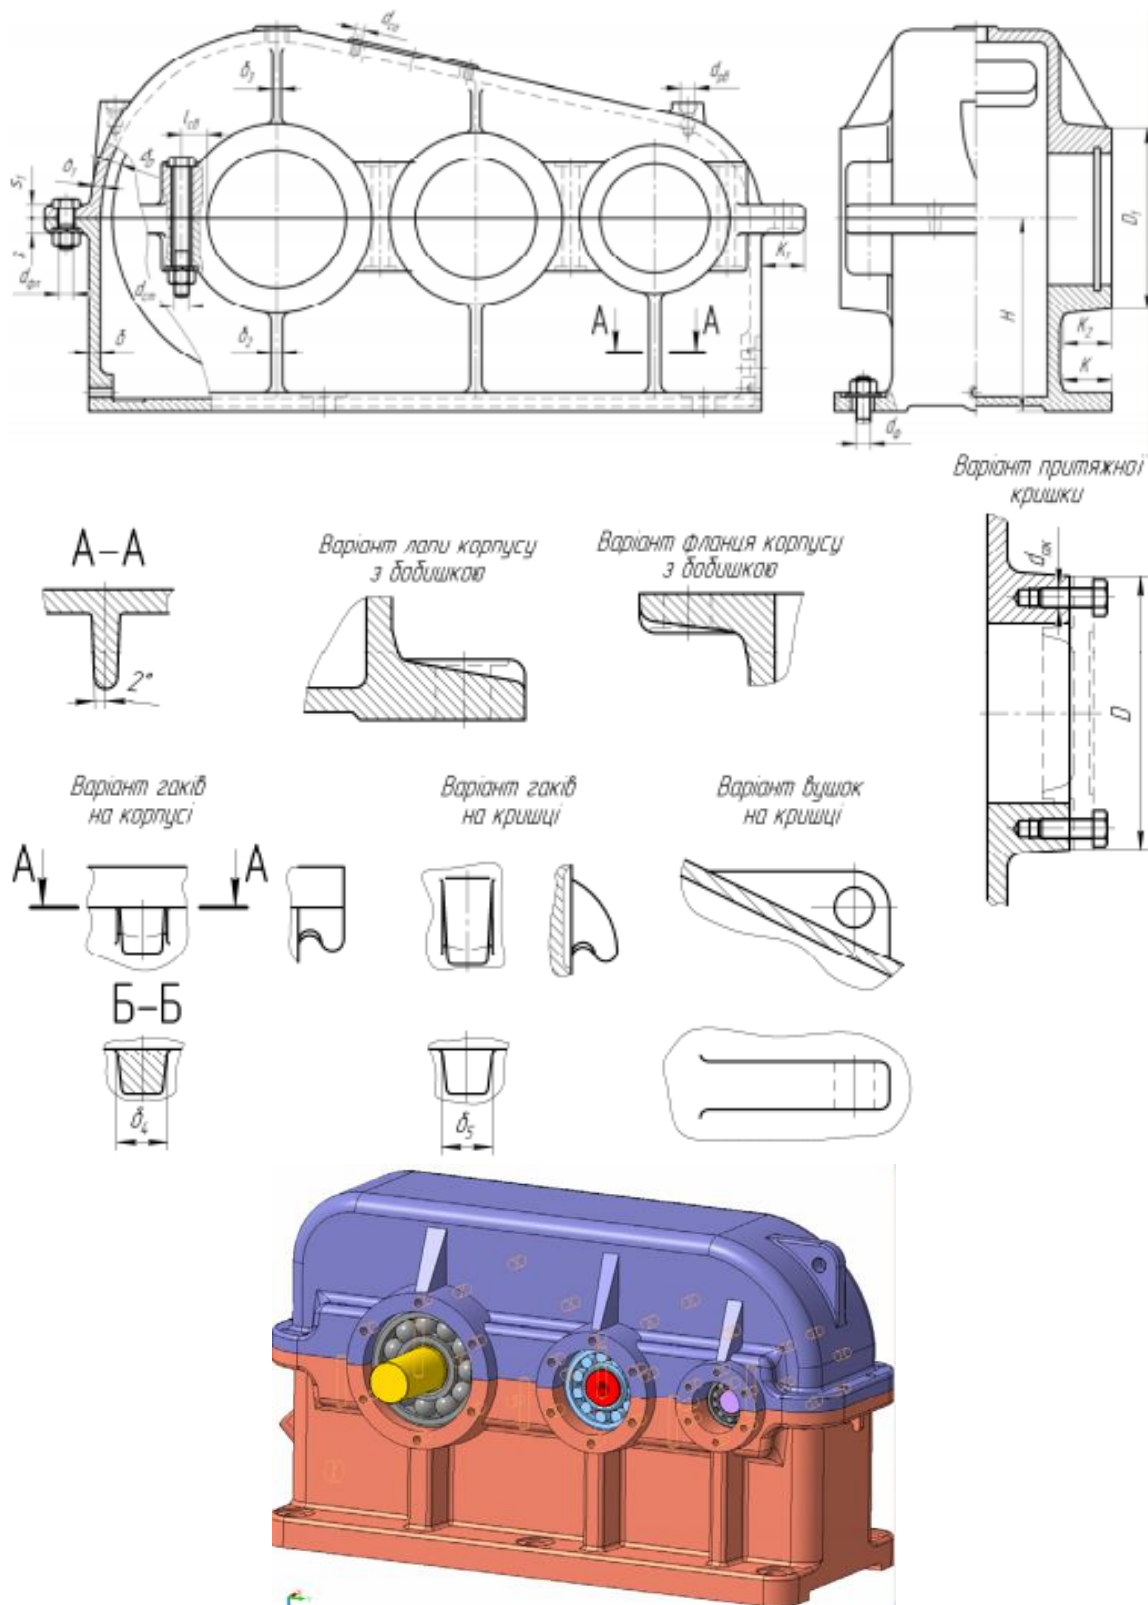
Розміри базових конструктивних елементів корпусних деталей (табл. 6.1)
